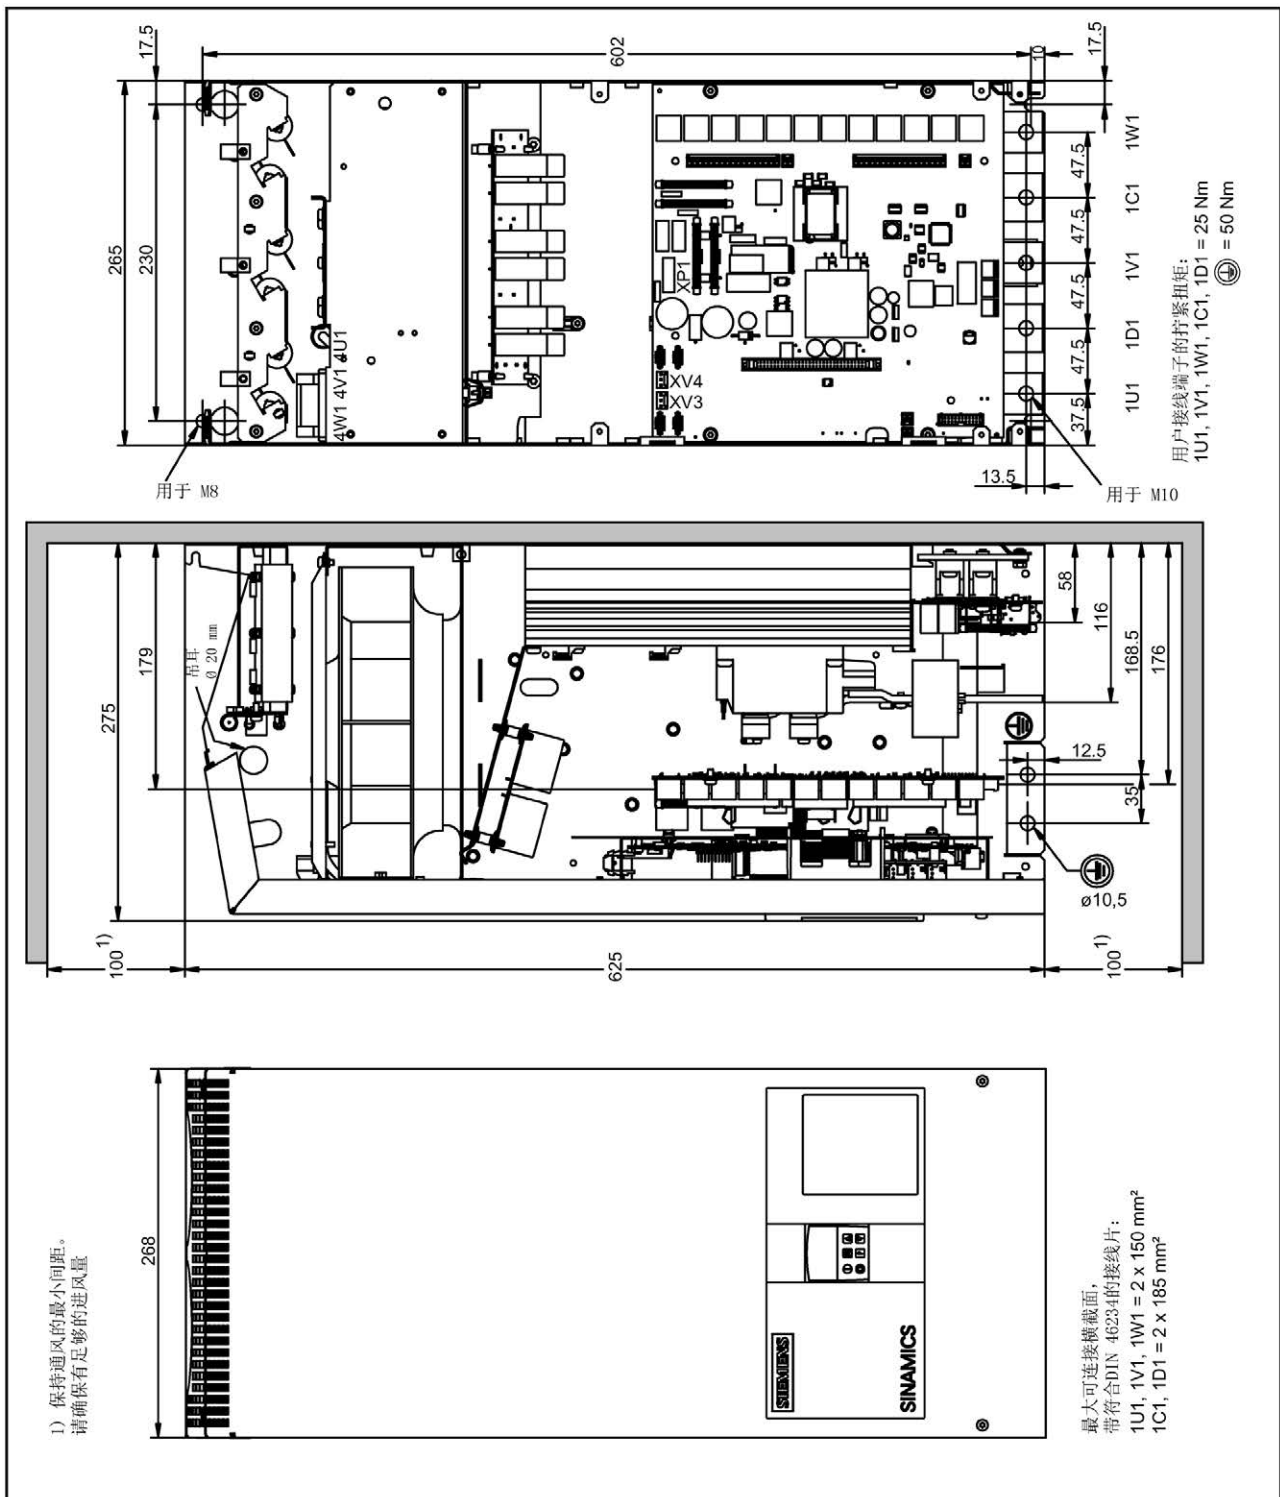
整流器 400 A~600 A, 2象限的外形尺寸图
